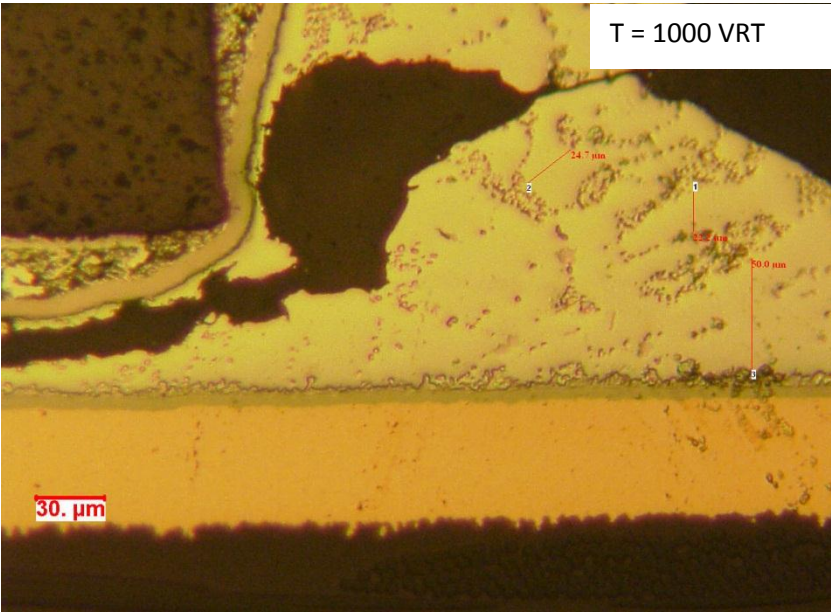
zoom de la figure IV-20 au niveau de la fissuration
